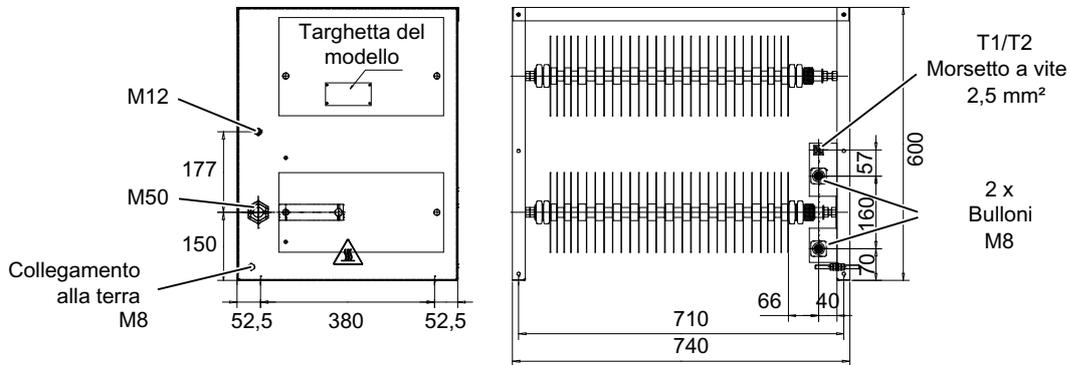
Disegno quotato - Resistenza di frenatura 25 kW / 125 kW
